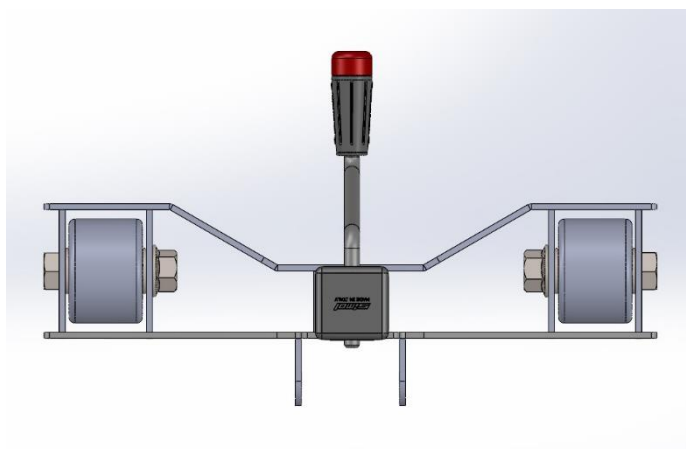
CAD-Konstruktion Hubarm Draufsicht
